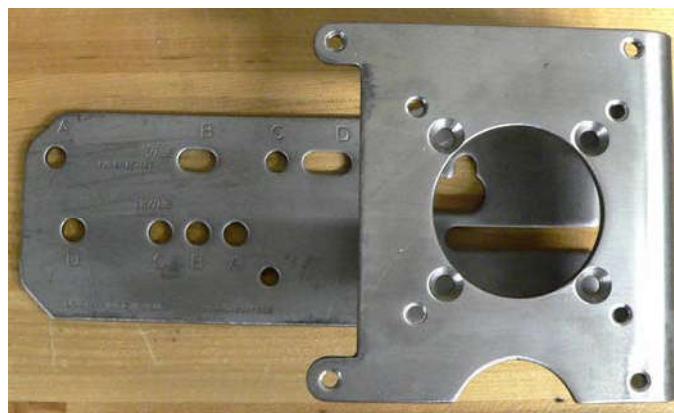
Монтажный кронштейн поршневого клапана для стандартного рычага
